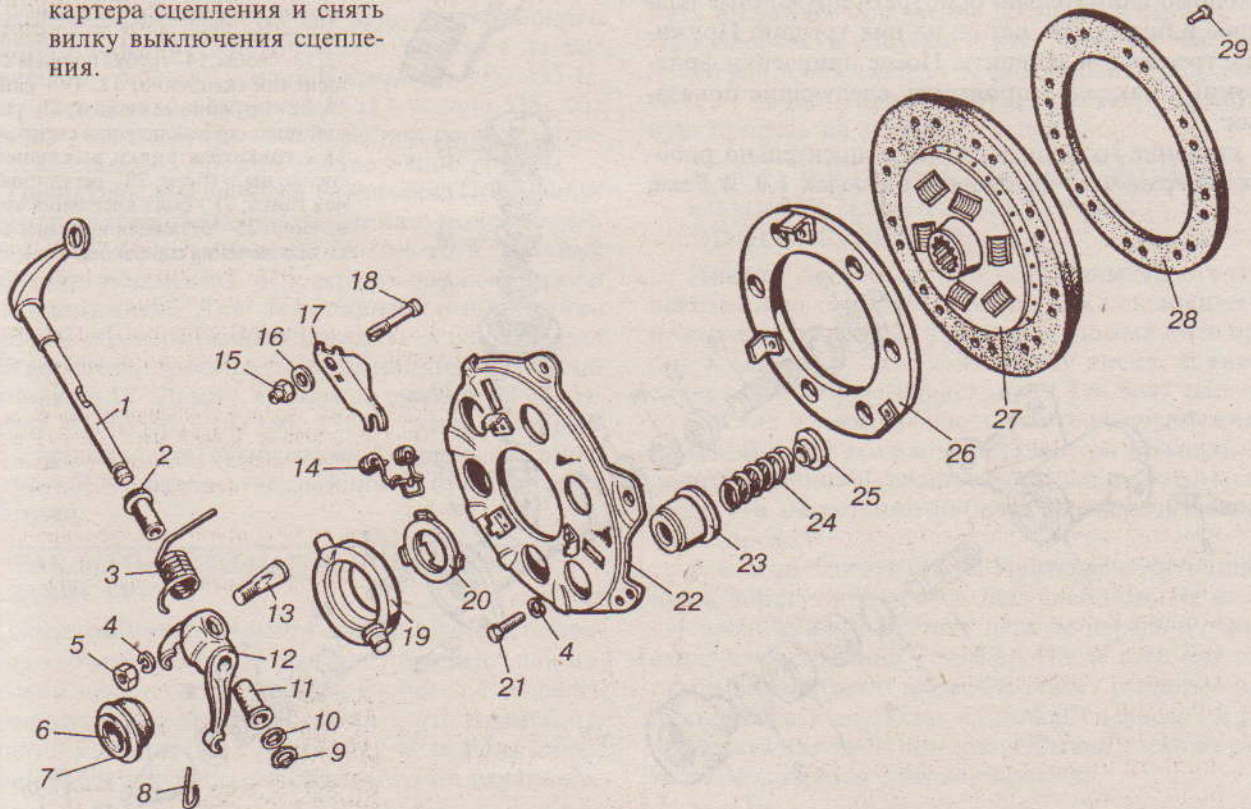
Сцепление автомобиля ЛуАЗ-969М: 1 - ось вилки выключения сцепления в сборе; 2 - втулка; 3 - пружина возвратная вилки выключения сцепления; 4 - шайба; 5 - гайка; 6 - манжета картера сцепления в сборе; 7 - пружина; 8 - звено соединительное подшипника и вилки выключения сцепления; 9 - кольцо; 10 - шайба опорная; 11 - втулка; 12 - вилка выключения сцепления; 13 - клин крепления вилки выключения сцепления; 14 - пружина пята соединительная в сборе; 15 - гайка регулировочная; 16 - шайба опорная регулировочной гайки сцепления; 17 - рычаг нажимной диска сцепления; 18 - палец нажимного диска; 19 - подшипник выключения сцепления; 20 - пята рычагов нажимного диска сцепления; 21 - болт; 22 - кожух сцепления в сборе; 23 - стакан нажимной пружины сцепления; 24 - пружина сцепления нажимная; 25 - прокладка; 26 - диск сцепления нажимной; 27 - диск сцепления ведомый с пластинами в сборе; 28 - накладка фрикционная ведомого диска сцепления; 29 - заклёпка
